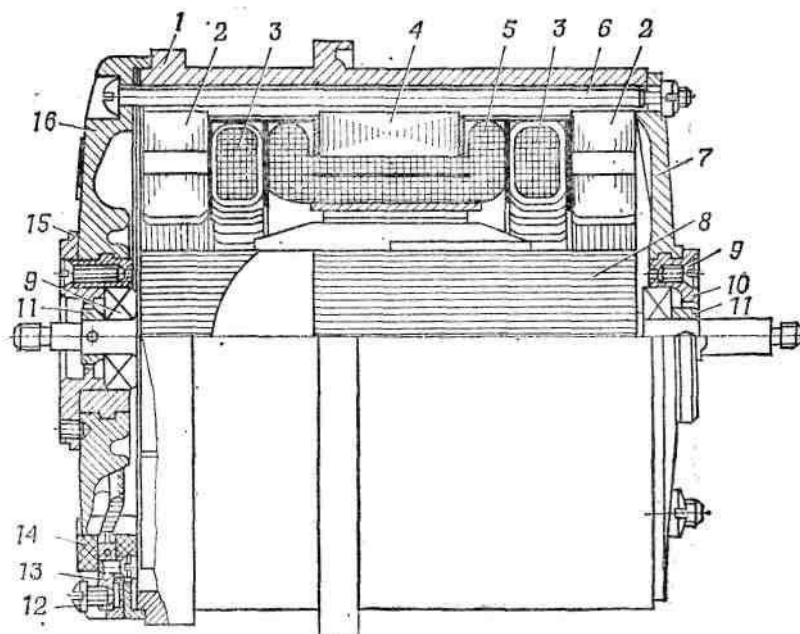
Бесконтактный сельсин БД-501А: 1 – корпус; 2 – тороид; 3 – катушка обмотки возбуждения; 4 – статор; 5 – обмотка статора; 6 – стяжной болт; 7 – задняя крышка; 8 – ротор; 9 – шарикоподшипник; 10 – крышка заднего шарикоподшипника; 11 – кольцо; 12 – контактный винт; 13 – клемма; 14 – клеммная колодка; 15 – крышка переднего шарикоподшипника; 16 – передняя крышка
